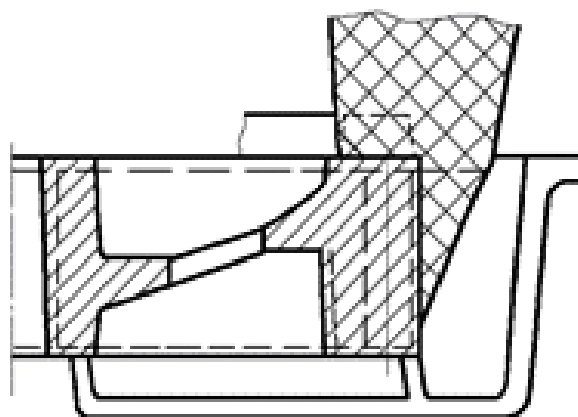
Подвод металла к отливке «Зубчатое колесо»:
